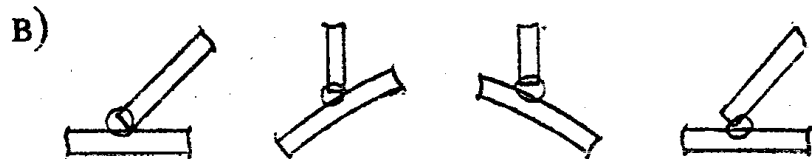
Сечения сварного шва в узловых соединениях
